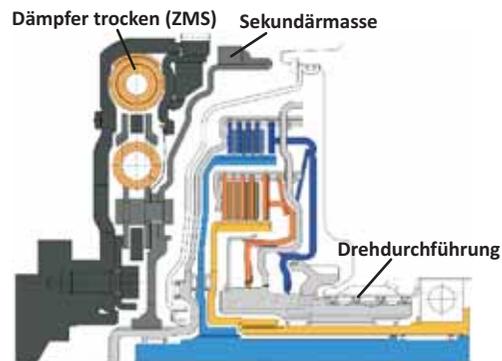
Nasse Doppelkupplung konventioneller Bauart, mit Drehdurchführungen zu den rotierenden Druckkolben
